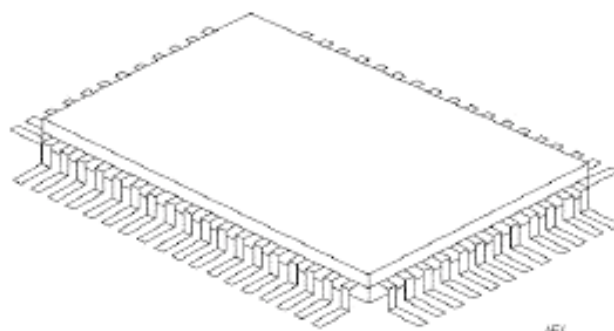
Конструкция корпуса типа PQFP (прямоугольный)
